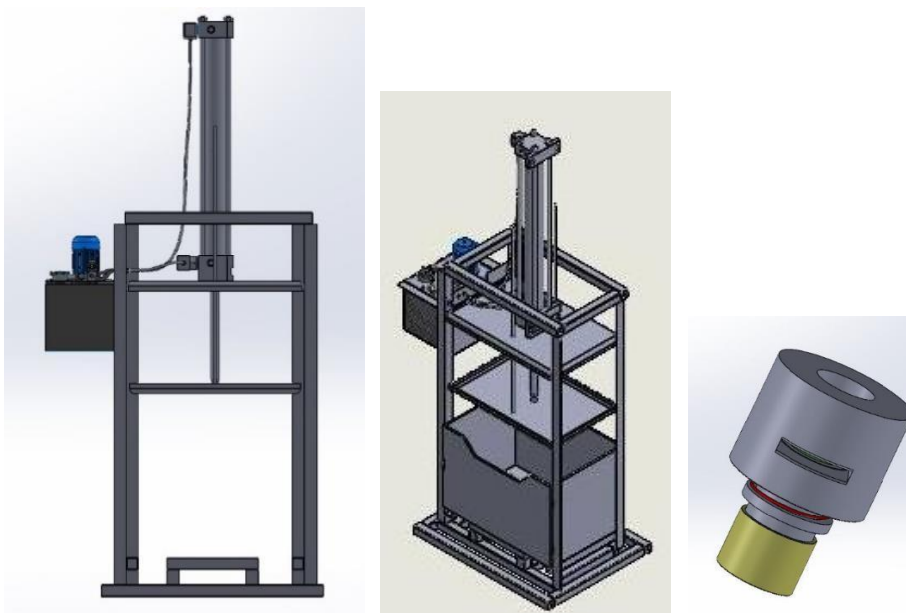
Vista frontal (izquierda), Vista isometrica (centro) y Valvula (derecha)
